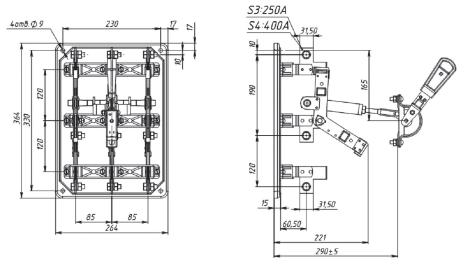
Б. Разъединитель типа П с центральным приводом на токи 250 А и 400 А
